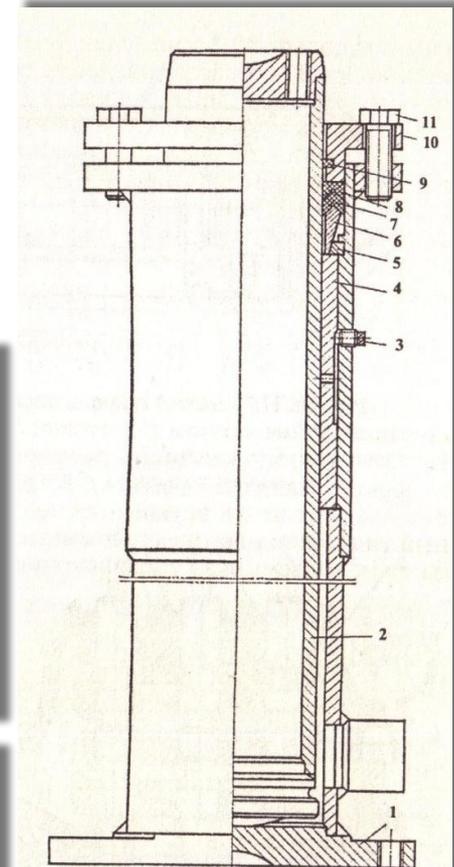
Плунжерный гидроцилиндр подъема каретки грузоподъёмника:
